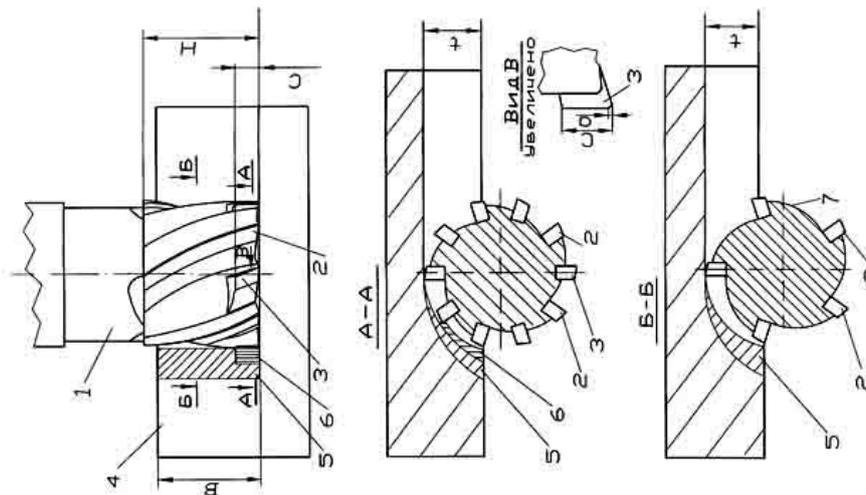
Конструктивная схема концевой фрезы с равной стойкостью торцовых режущих лезвий, в которой у торцовой части имеют затылки только стандартные зубья.
